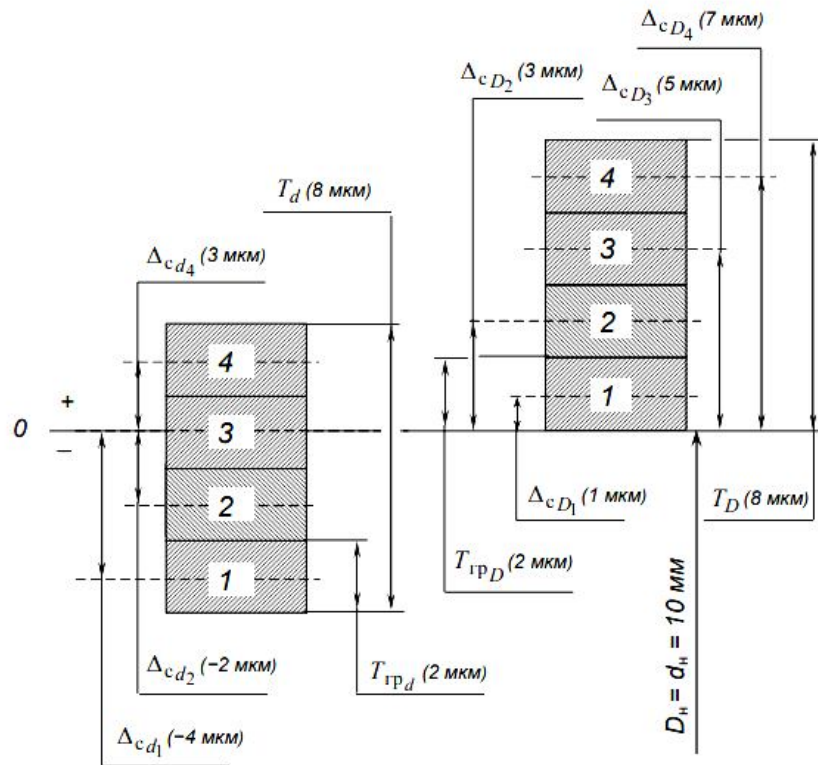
Схема розташування полів допусків діаметрів отвору в гільзі (D) і робочій поверхні плунжера (d)
